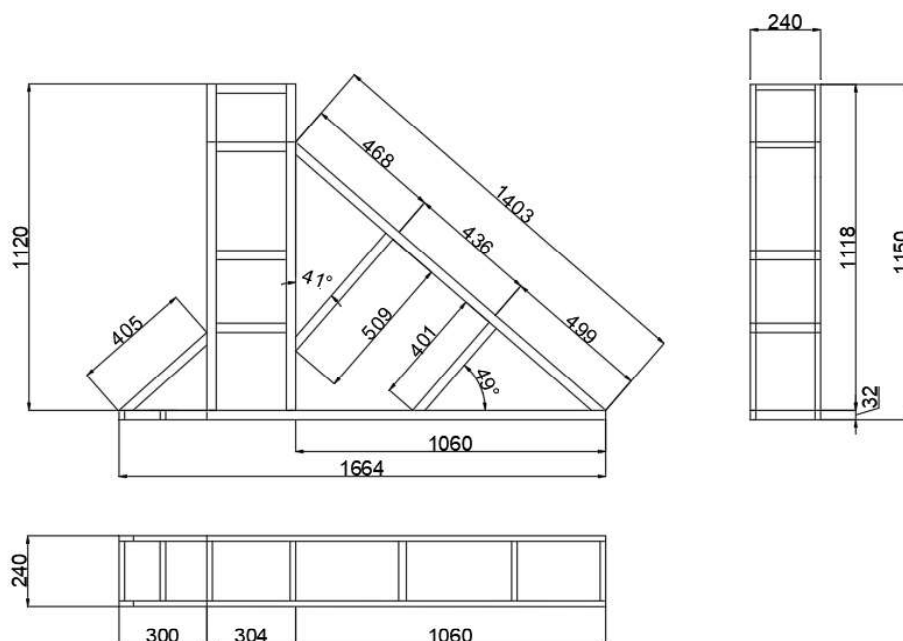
29 - Estrutura fabricada para ensaio de flexão em engaste
